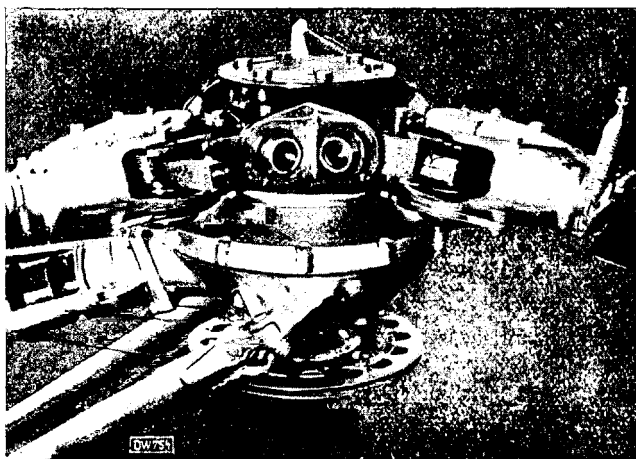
Schraubennabe mit den Steuerteilen für die Blattbewegung
